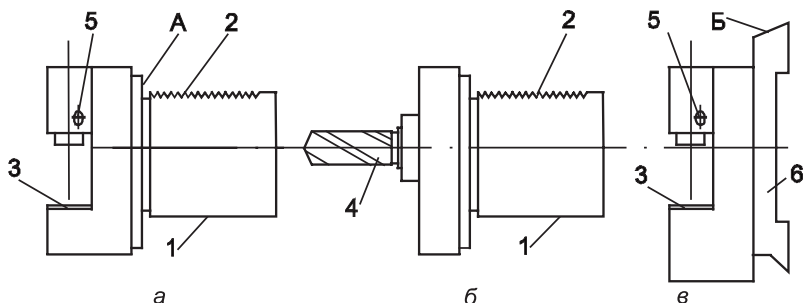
Допоміжний інструмент: *а, в* — під призматичні різці; *б* — під інструмент для внутрішньої обробки
